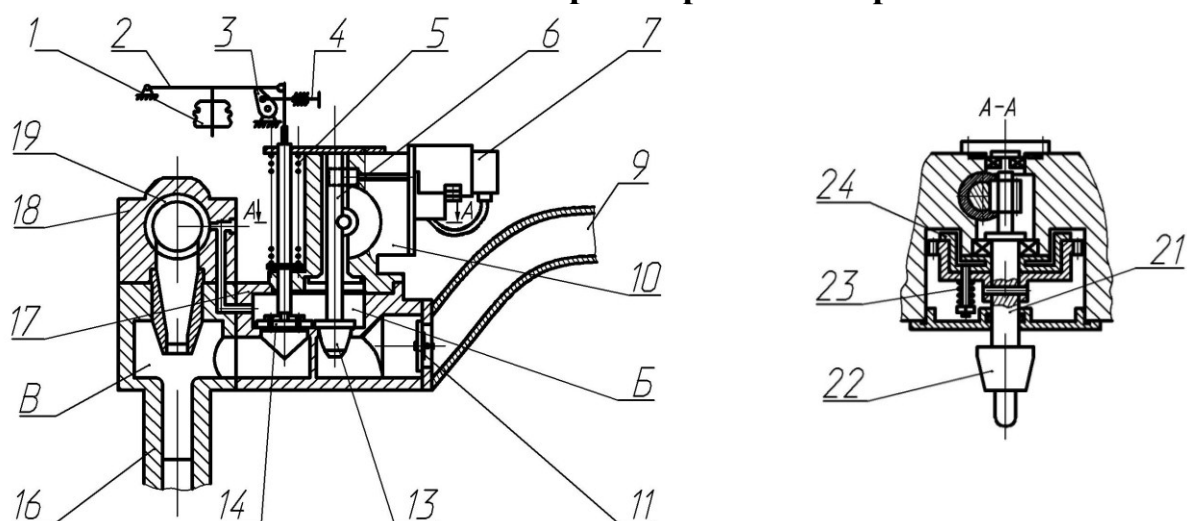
Водоструйный насос: 1 -- сильфон; 2 - рычаг; 3 - кулачок; 4 - ручка для открытия отсечного клапана при сливе воды; 5, 23- пружина; 6- рейка; 7 - электродвигатель; 9 - патрубок; 10 - редуктор; 11- клапан обратный; 13 - клапан дозирующий; 14 - клапан отсекающий; 16 -
